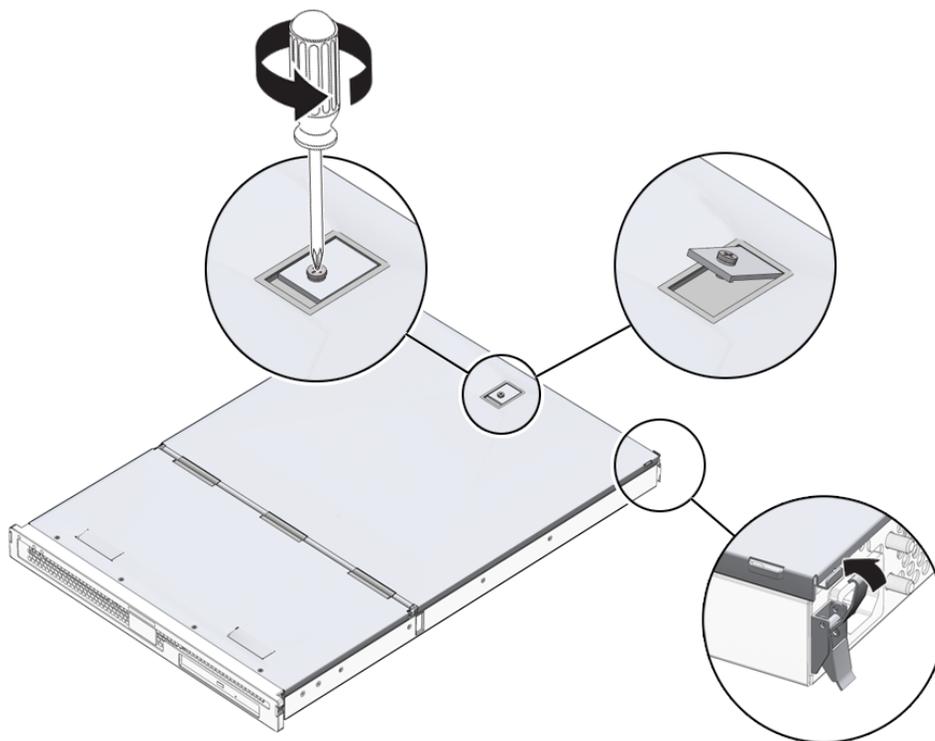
Emplacement de la vis captive et des mécanismes de fermeture latéraux sur la section arrière du capot
